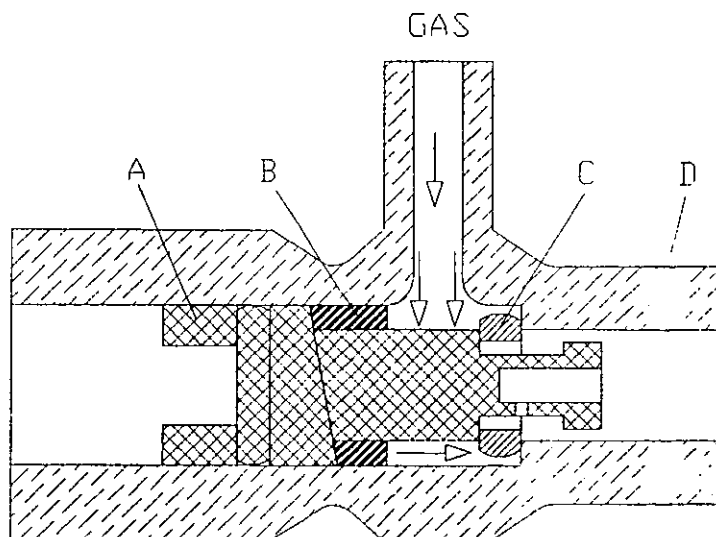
Corte transversal de válvula de helicoidal (cerrada)
